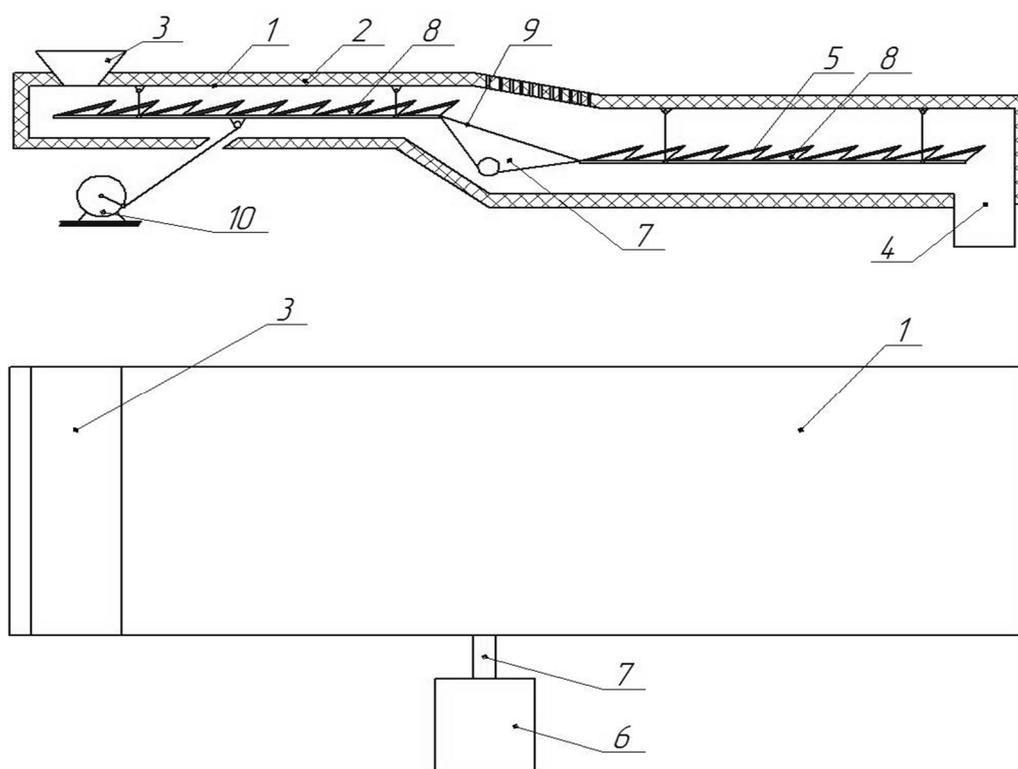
Устройство для сушки зерна: 1 – кожух; 2 – теплоизолирующий материал; 3 – загрузочный бункер; 4 – выгрузное окно; 5 – нагревательные элементы; 6 – вентилятор; 7 – воздуховод; 8 – транспортирующий рабочий орган (ТРО); 9 – скатная доска; 10 – привод
